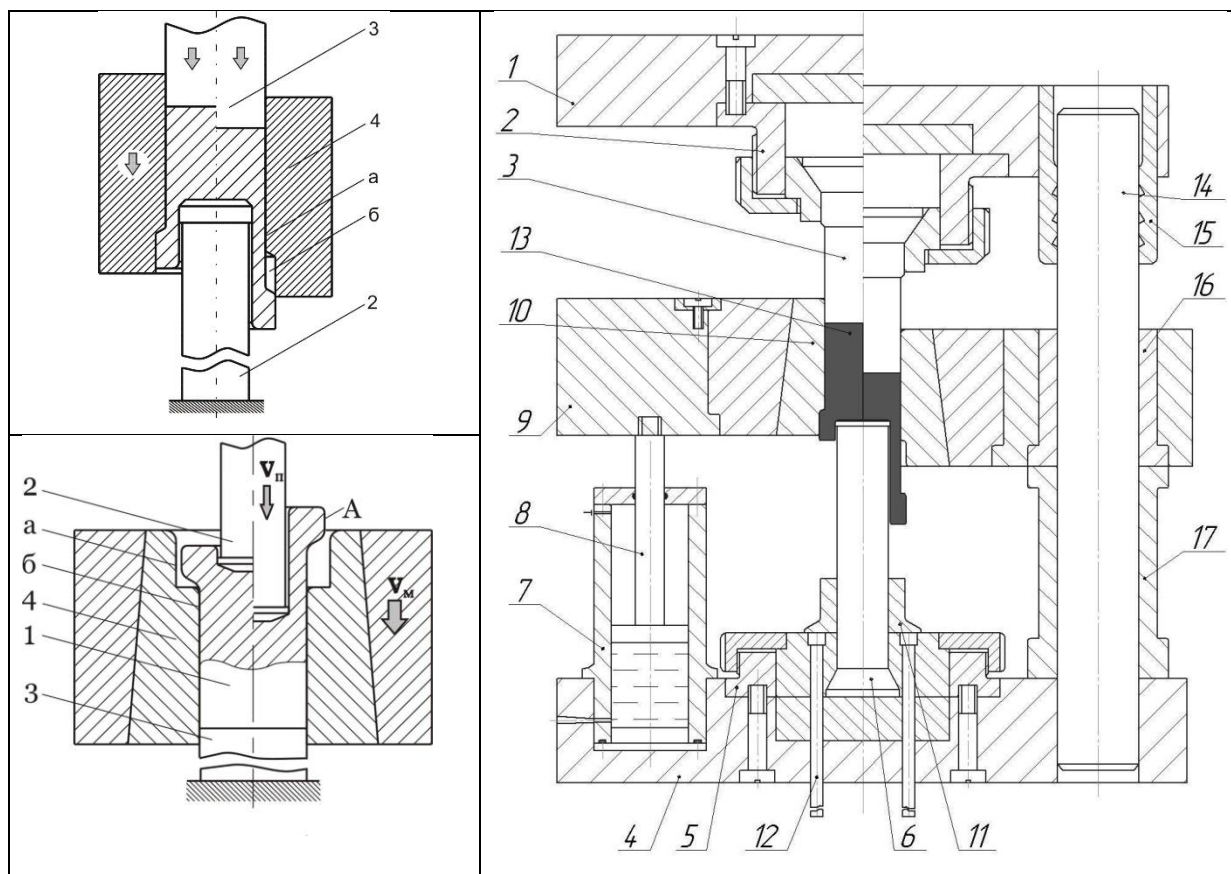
Схема штампа для реалізації способу комбінованого видавлювання порожнистих деталей с перемінною товщиною стінки
